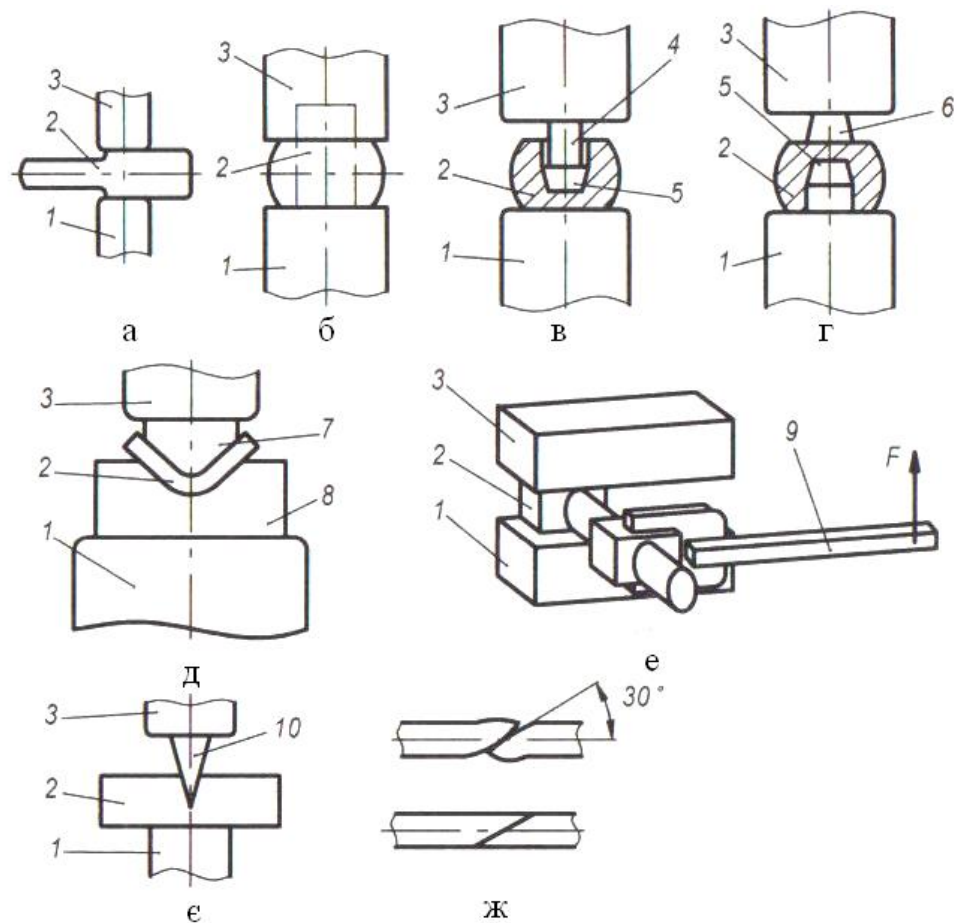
Схеми різних операцій кування: а – видовження; б – осадка; в, г – прошивання; д – згинання; е – закручування; є – рубання; ж – ковальське зварювання; 1 – нижній ударник; 2 – заготовка; 3 – верхній ударник; 4 – надставка; 5, 6 – прошивка; 7, 8 – половини підкладного штампа; 9 – вилка; 10 – сокира; F – сила
